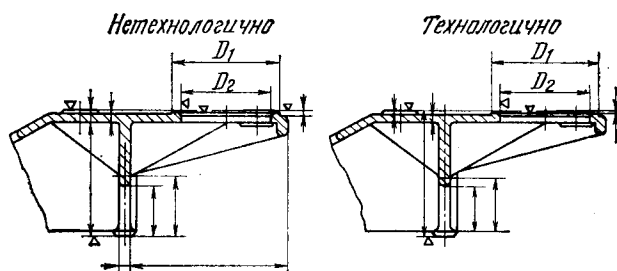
Увязка обрабатываемых поверхностей с базовыми.
